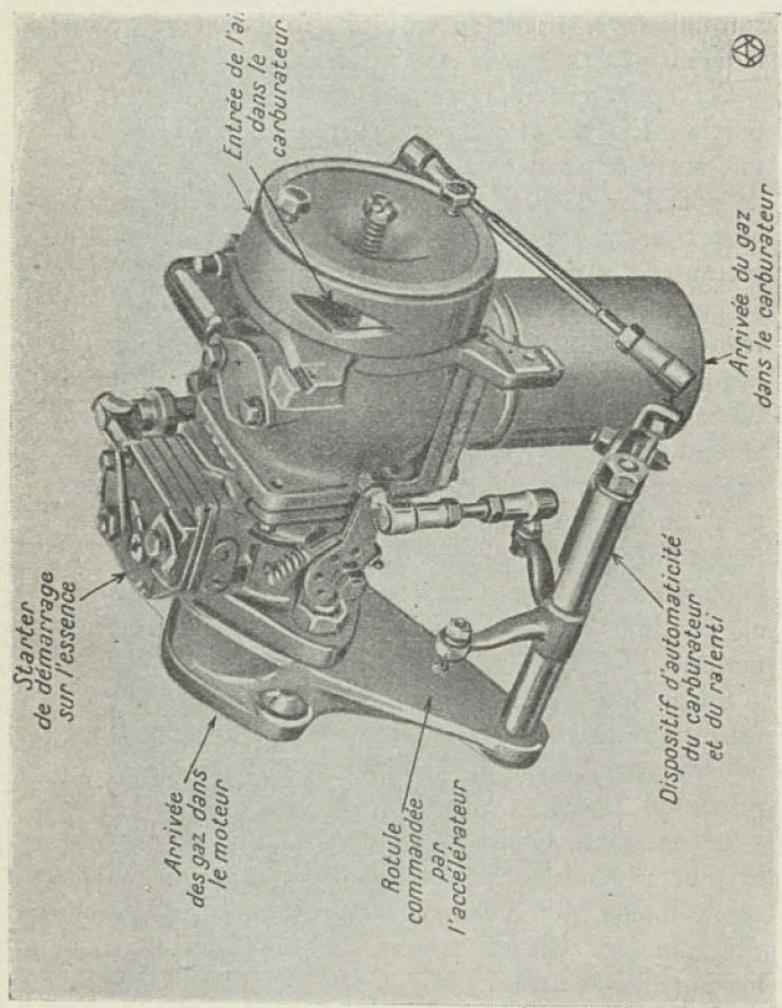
Carburateur-mélangeur Latil M3 G.
